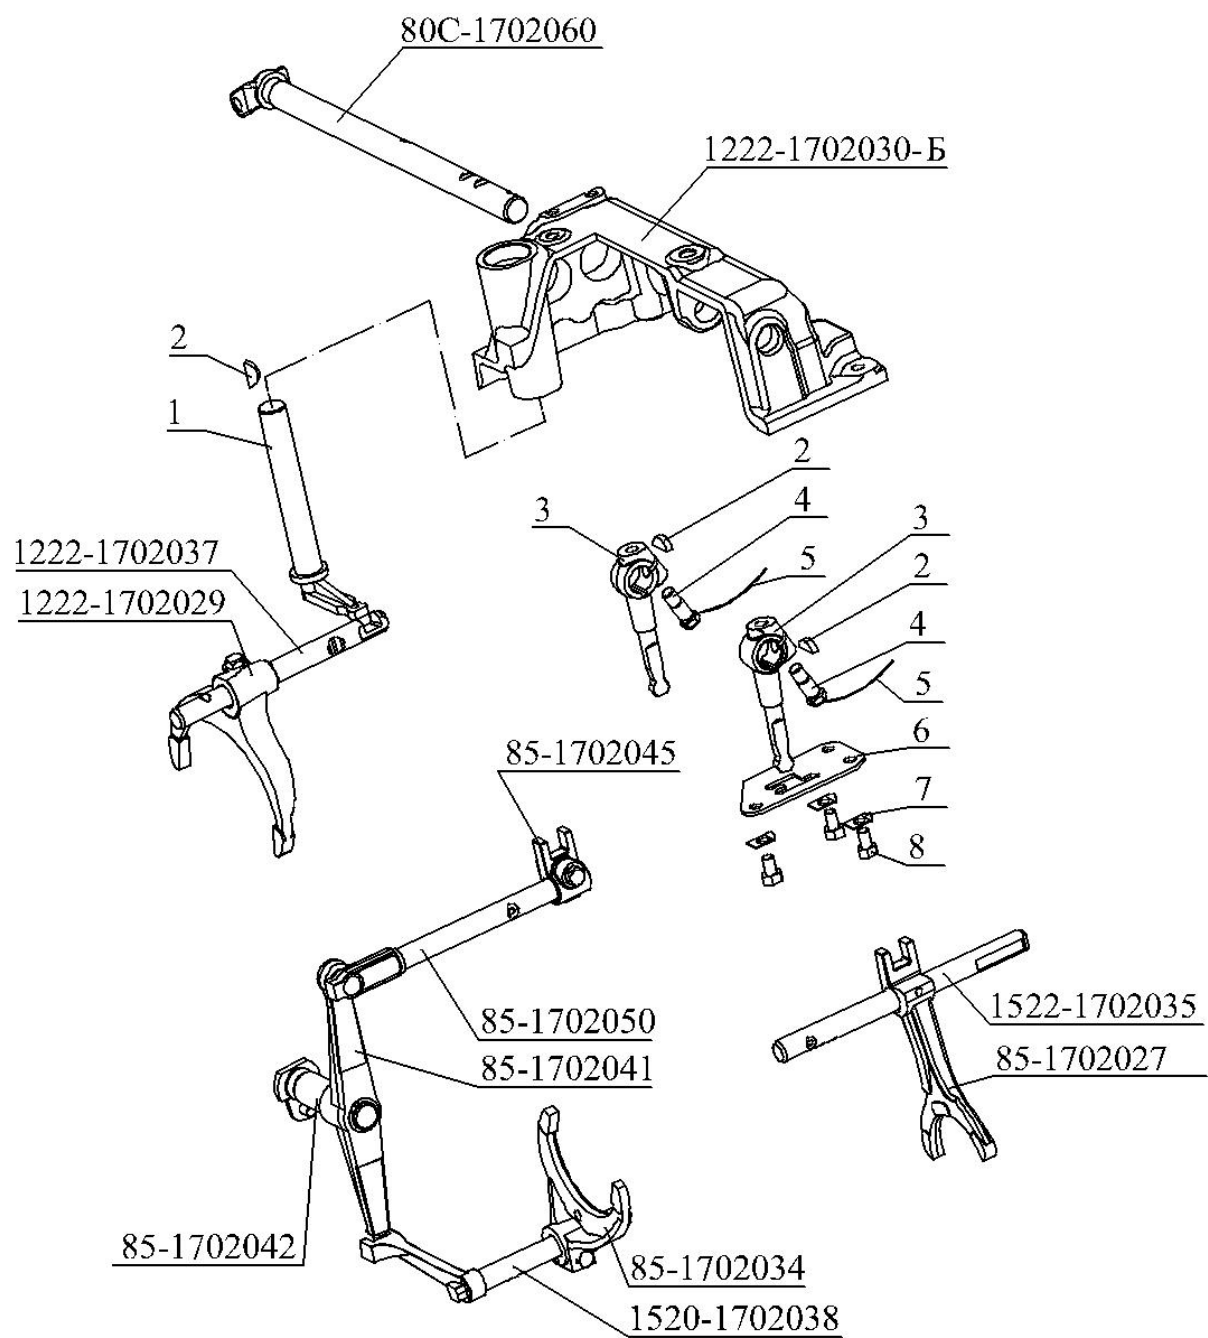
Механизм управления коробкой передач (лист 1 из 3)
